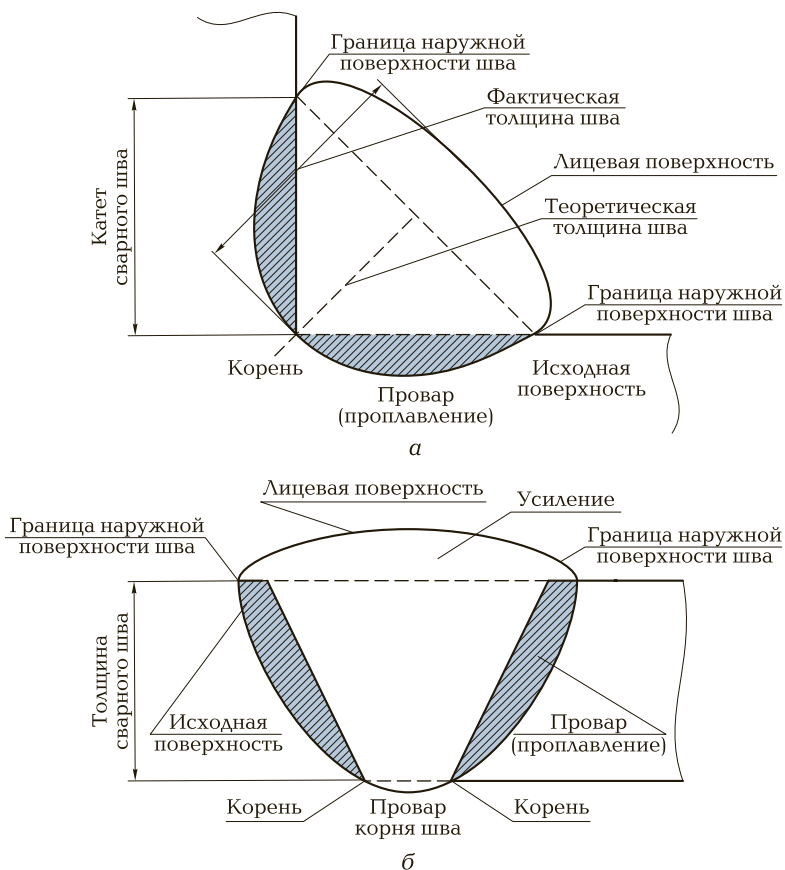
Конструктивные элементы углового (а) и стыкового (б) сварных швов
